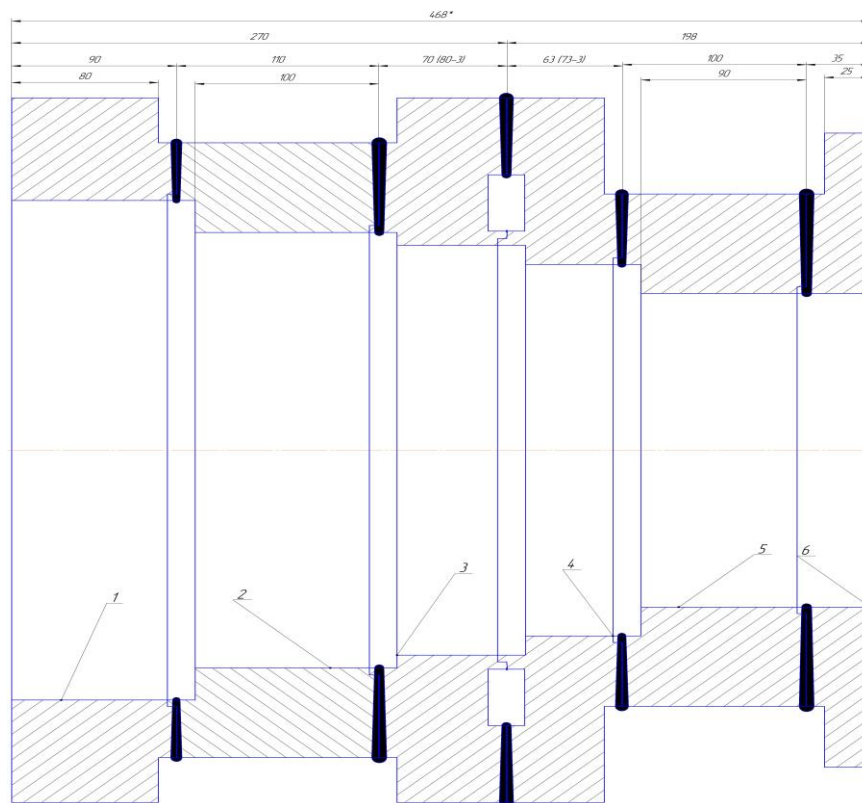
Эскиз сварной заготовки шпангоута (Этап №3)
